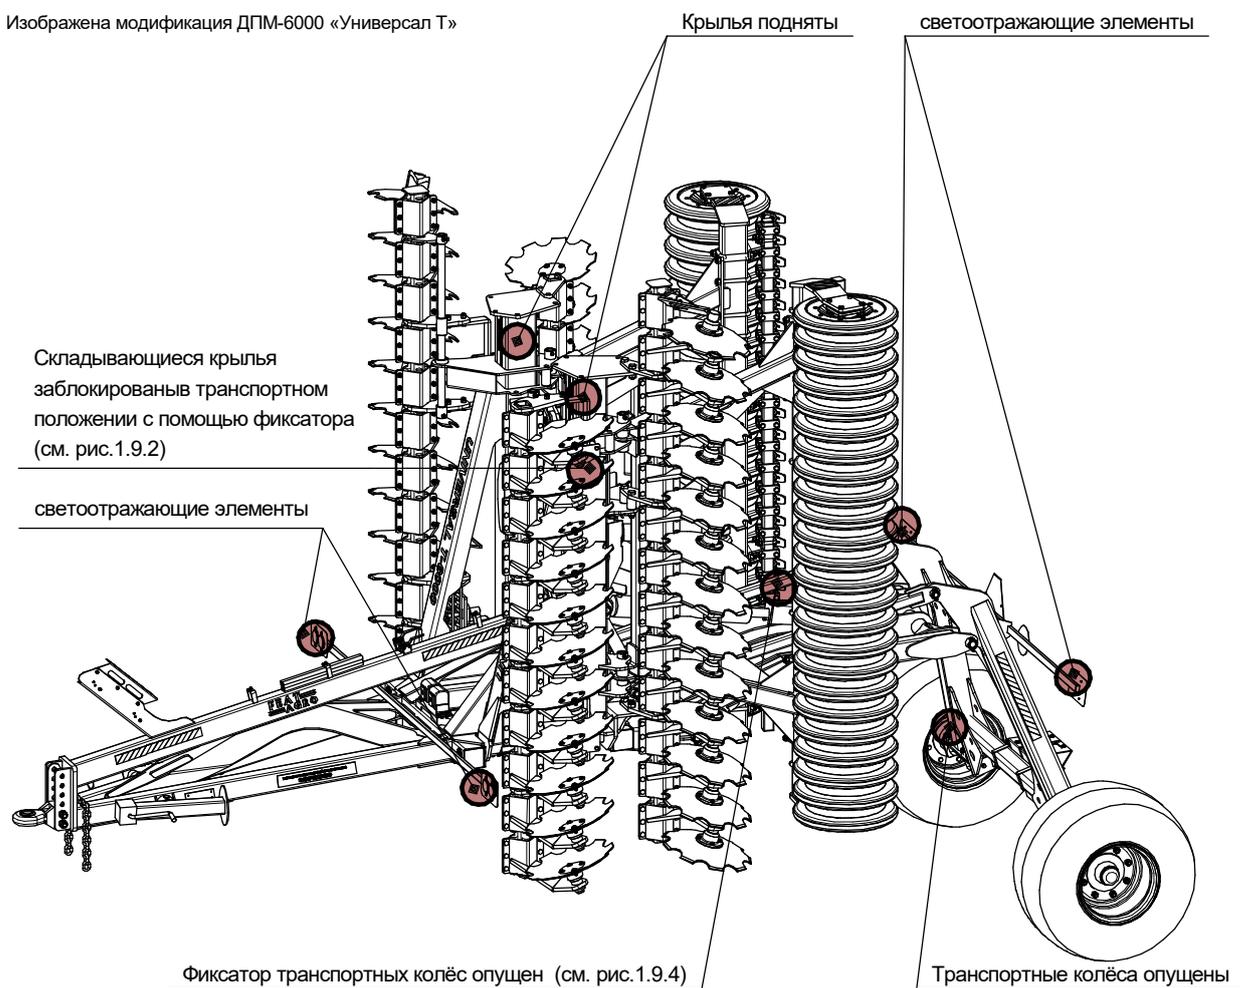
Транспортное положение дисковой почвообрабатывающей машины ДПМ "Универсал" / "Универсал Т"
